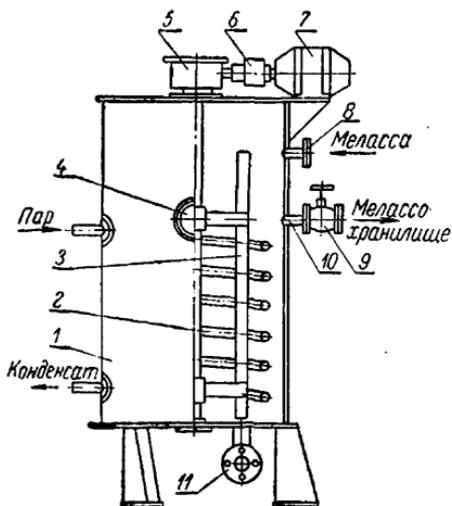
Смеситель мелассы-карбамида СМК-0,5.
